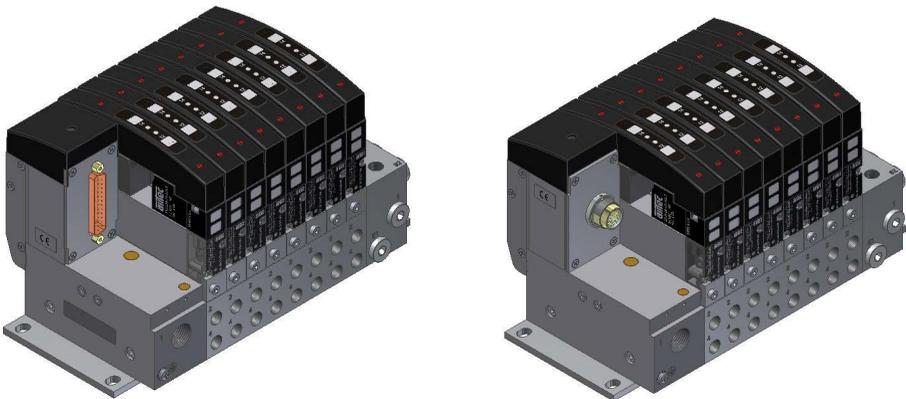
RE-46/08-M-1-000 und RE-46/08-M-3-000 inkl. RE-46-B-01, BefestigungsfüÙe für Flanschmontage
